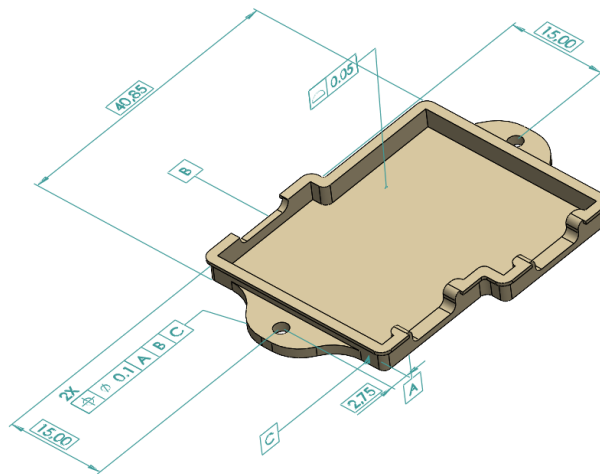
Tolerancias geométricas “Carcasa TP4056”
